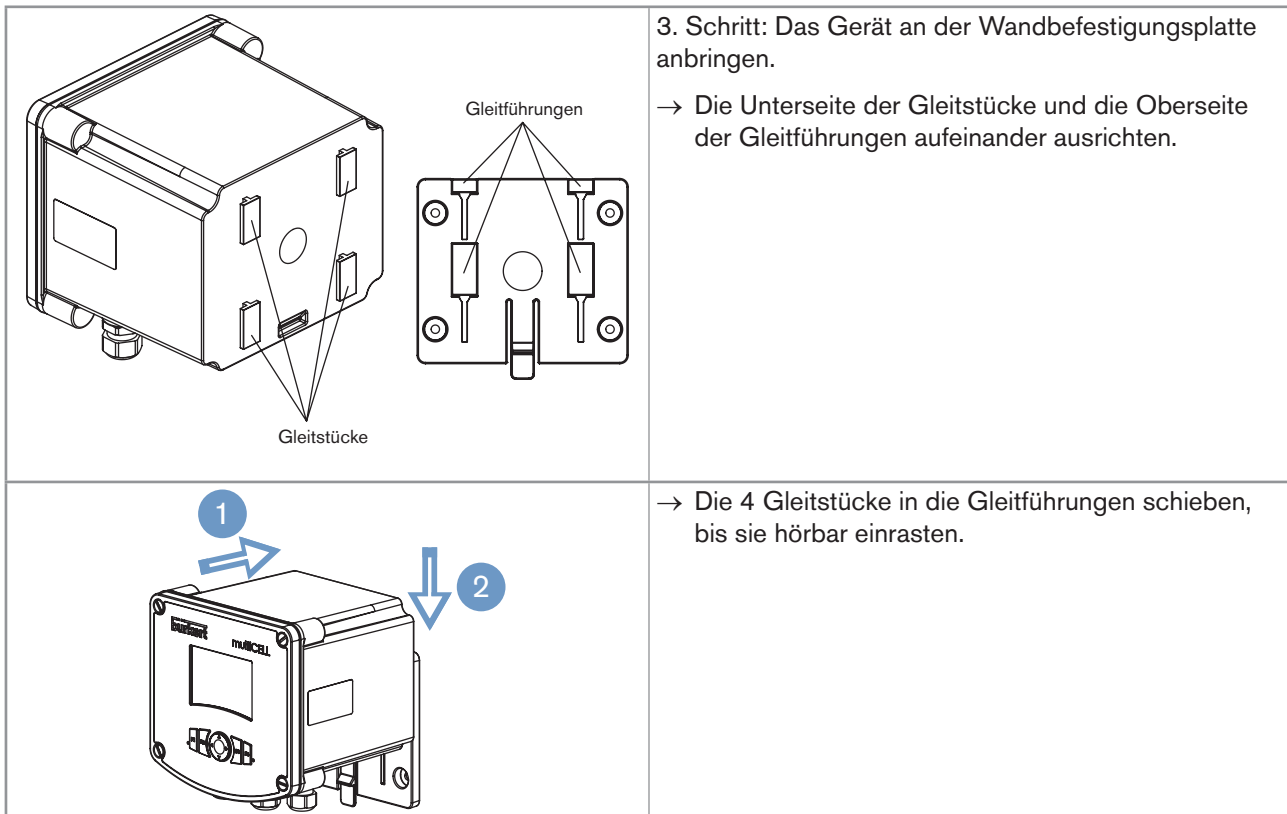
Installation eines Geräts für Wandmontage an einem Trageelement
